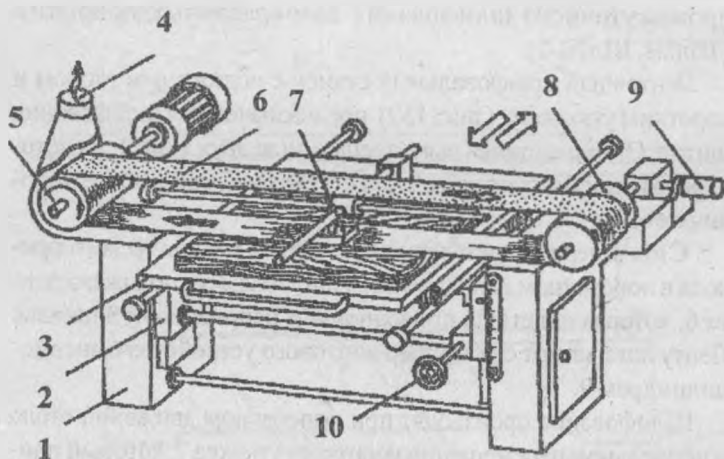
Ленточный шлифовальный станок с подвижным столом:
